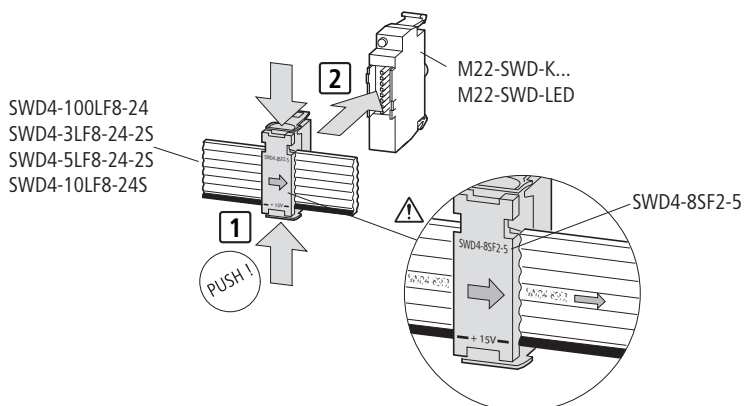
Collegamento dell'elemento funzionale al cavo piatto SWD
